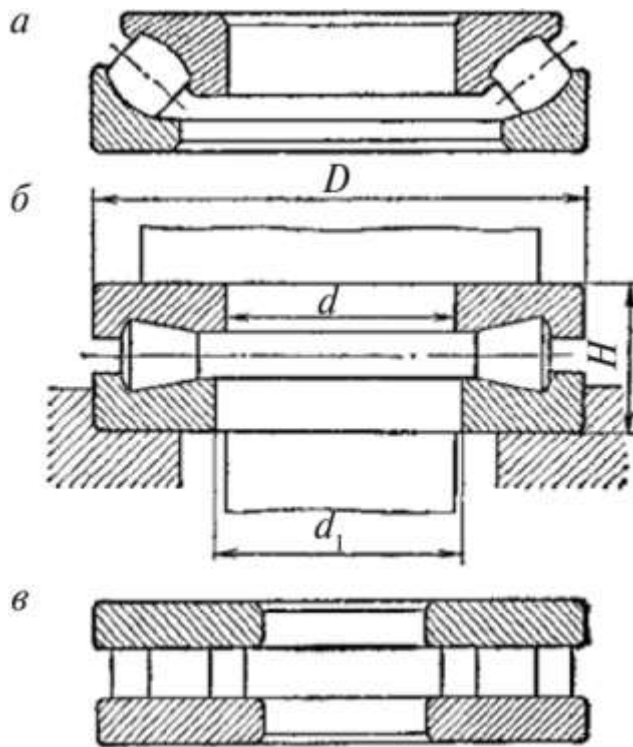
Роликоподшипники: *a* — упорно-радиальные со сферическими роликами; *б* — упорные с коническими роликами; *в* — с цилиндрическими роликами
